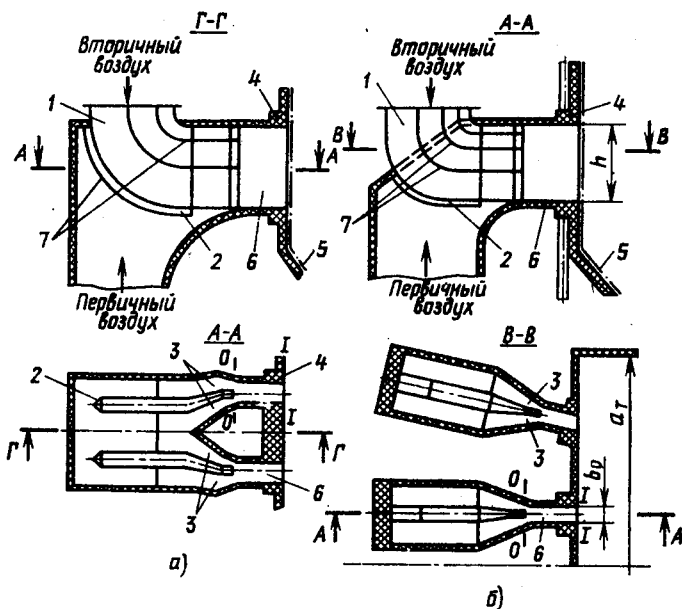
Конструктивные схемы вихревых горелок для сжигания газа и мазута:
